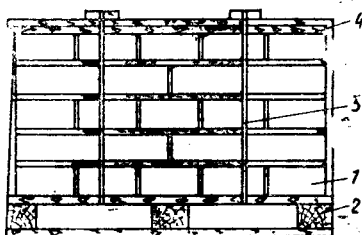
Пакет головок блоков цилиндров автомобиля ЗИЛ-130:
